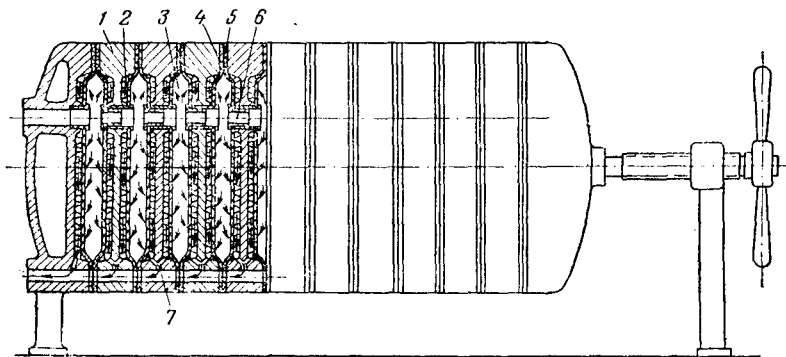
Фильтрпресс с вертикальными камерами (камерный фильтрпресс):
